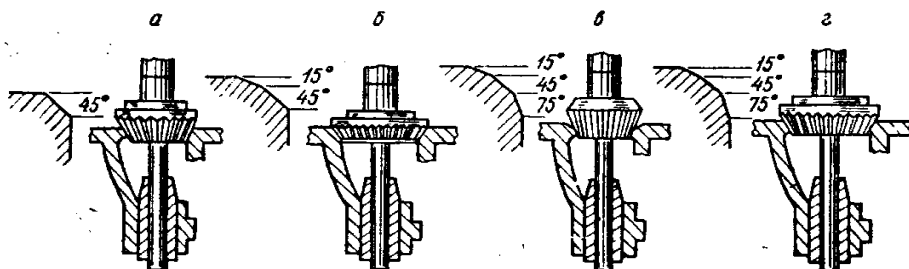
Обробка клапанного гнізда фрезами. Фрезерування під кутом
